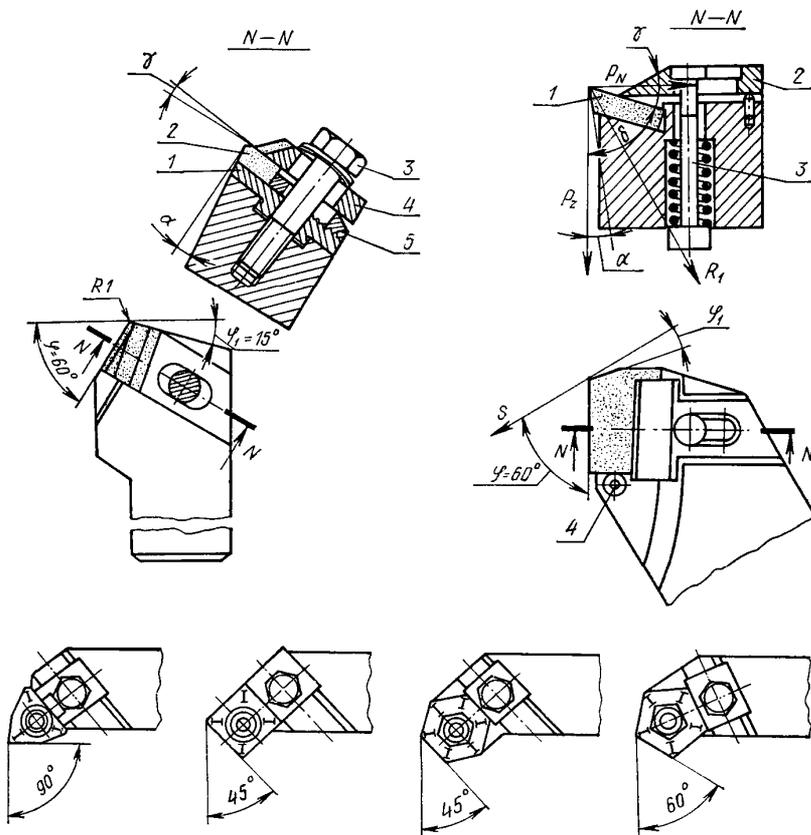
Резцы с механическим креплением твердосплавных пластин:
